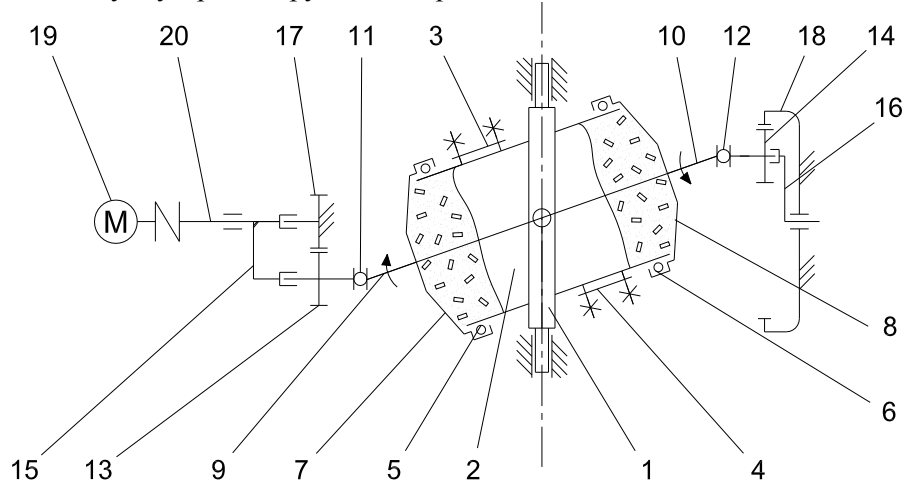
Установка для вибрационно-вдцентровой обработки: 1 – карданный подвиг, 2 – цилиндричная вставка, 3 - завантажувальний люк, 4 - розвантажувальний люк, 5 і 6 – опори, 7 і 8 – напівбарабани, 8 і 9 – вали, 11 і 12 - карданні передачі, 13 і 14 – сателіти, 15 і 16 – водила, 17 і 18 - центральні колеса, 19 – електродвигун, 20 - ведучий вал
